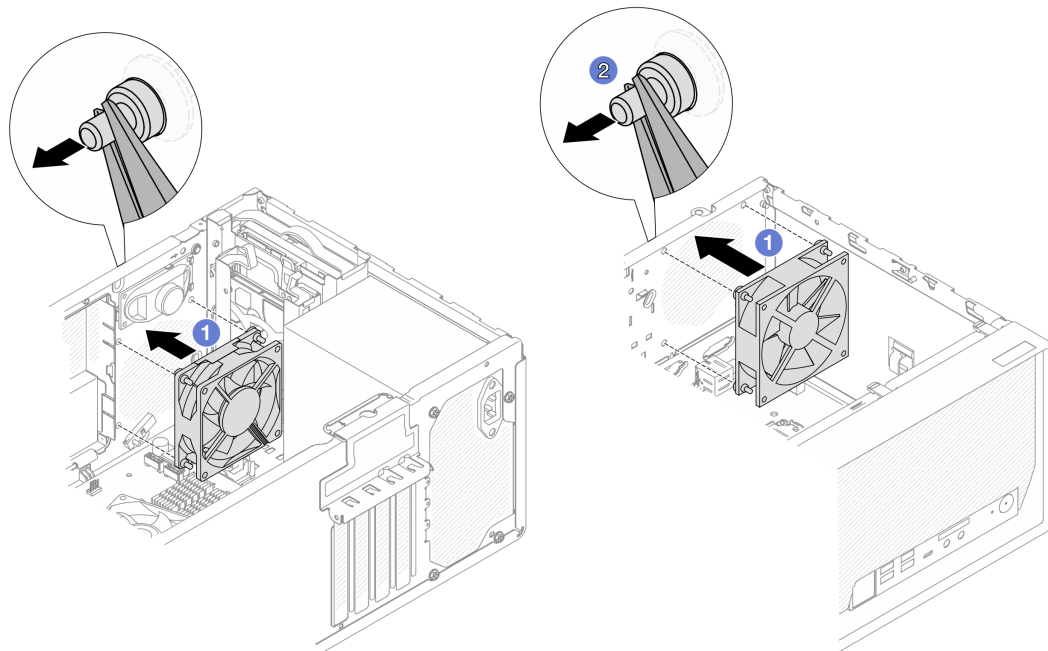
Installation du ventilateur avant ou du ventilateur arrière
